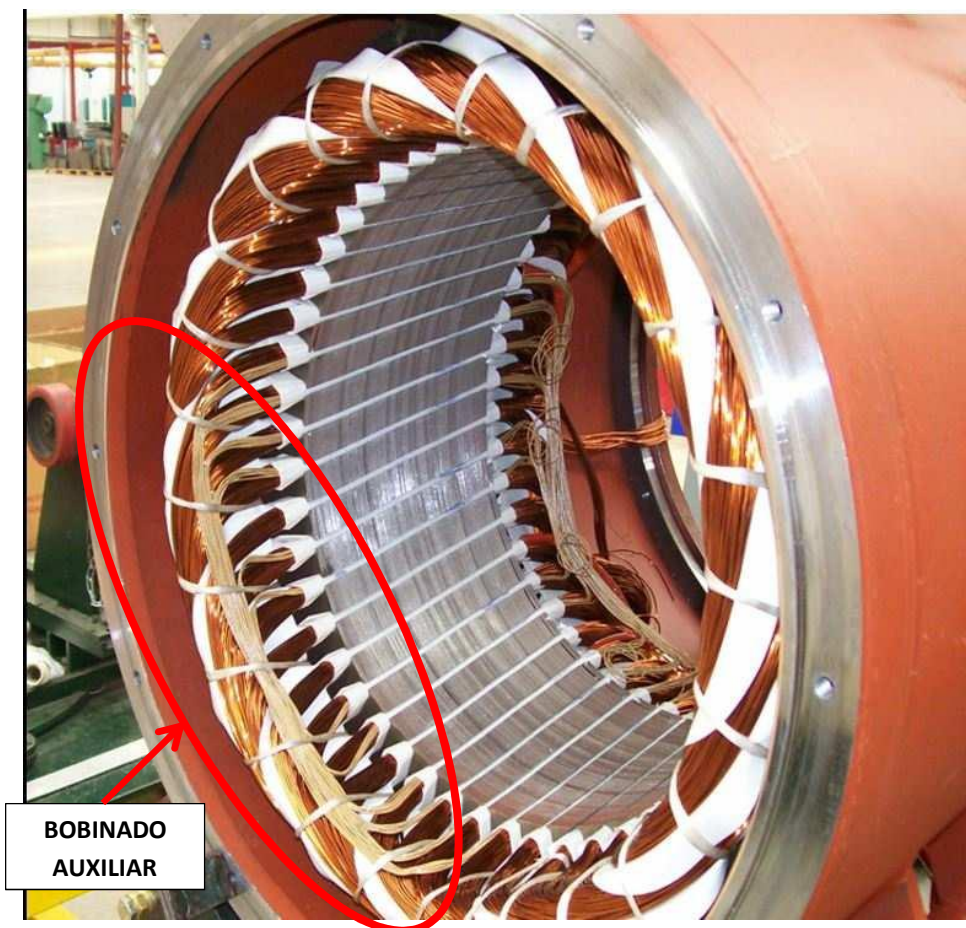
Disposición del bobinado auxiliar en un alternador de Cramaco
